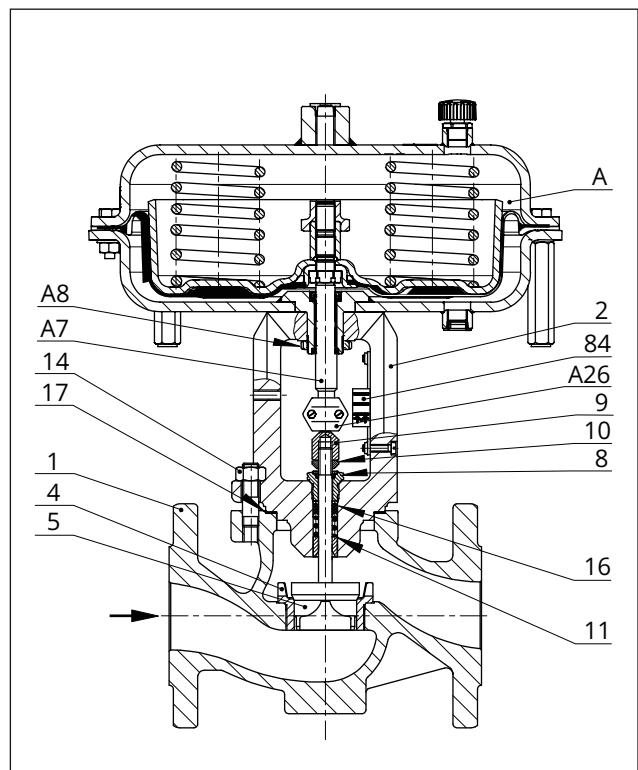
Регулирующий клапан Tun 3241-1 с пневматическим приводом Tun 3271, корпус до DN 150/NPS 6
